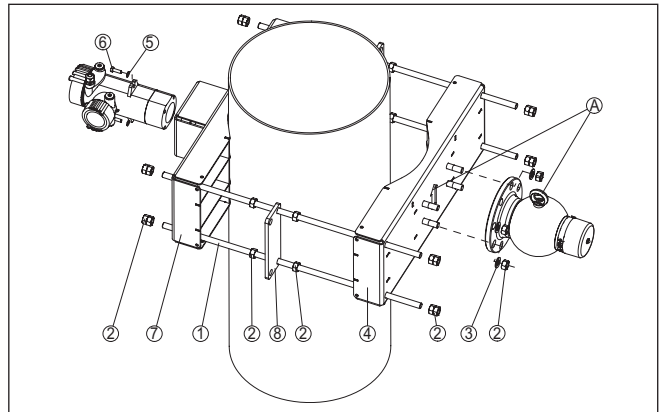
Dispositivo de sujeción KV 31 con sensor montado horizontalmente
